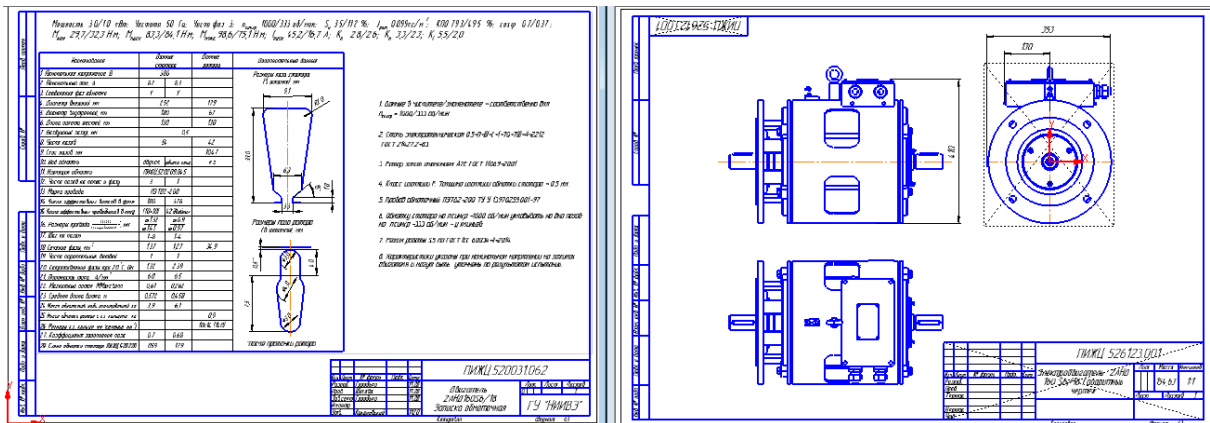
Обмоточная записка и габаритный чертёж электродвигателя 2АНД 160 S6/180
